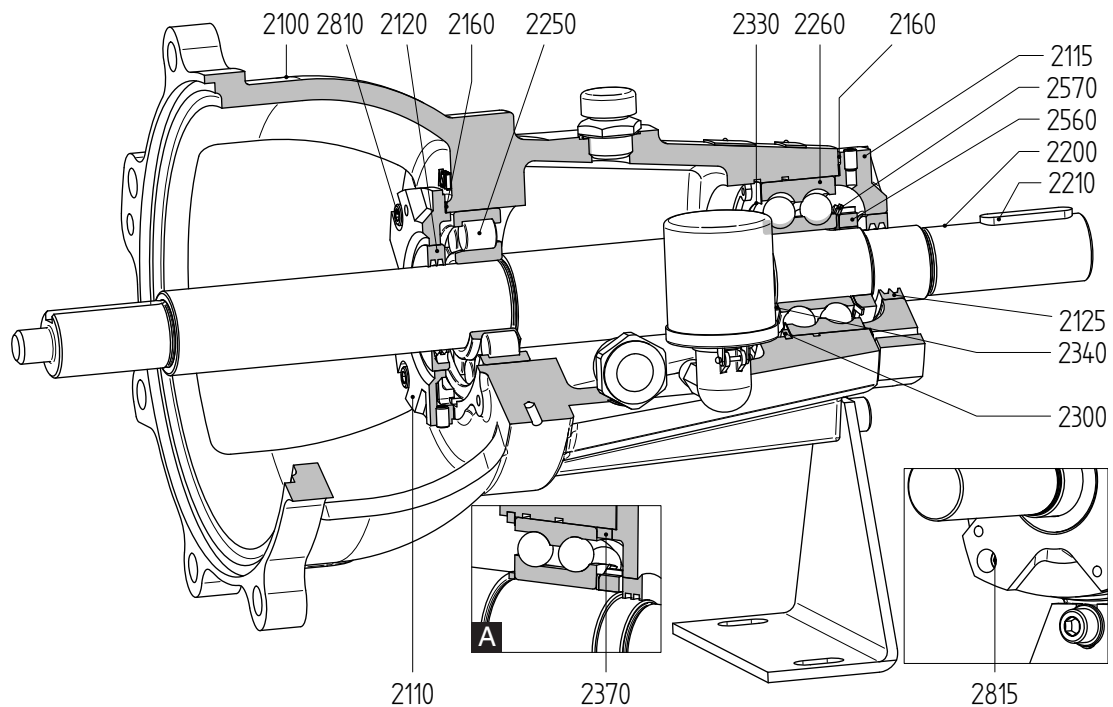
Palier L4 (renforcé, huilé) (A = groupe de palier 3).
